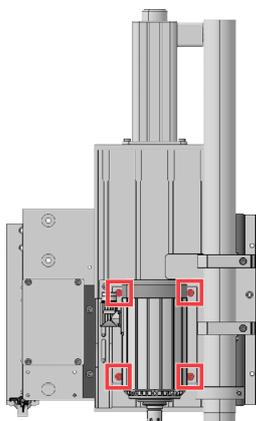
FESTSCHRAUBEN DER SCHRAUBEN
